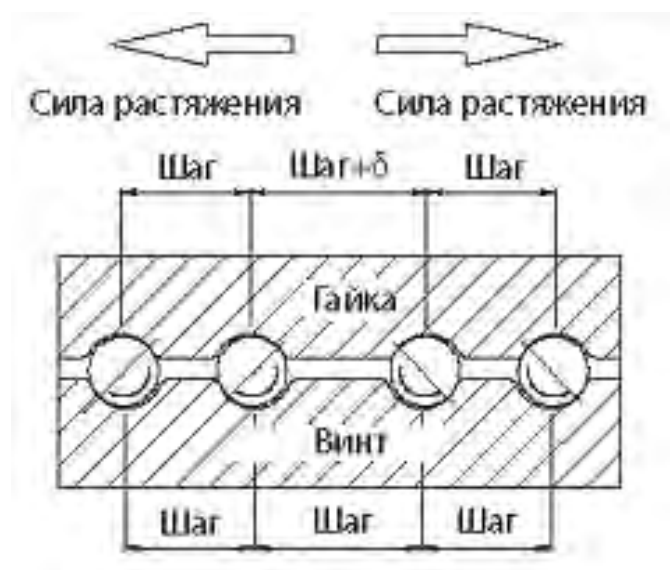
Преднатяг, полученный шлифовкой внутренних канавок гайки
